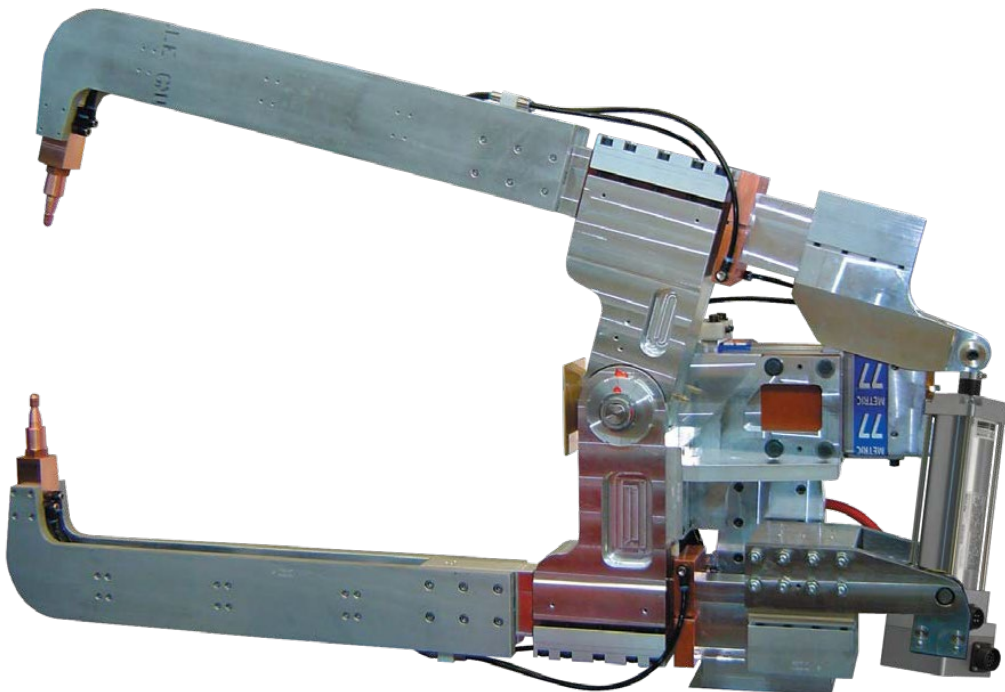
Beispiel eines ServoWeld-Aktuators, der an einer "X"-Style-Schweißzangeneinheit installiert ist.
